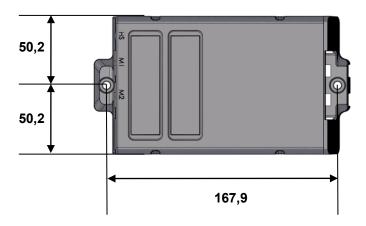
Montagemaße: Steuerung SMART (Angaben in mm)
